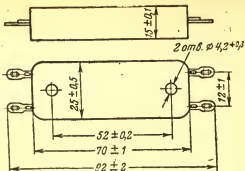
Габаритный чертеж столбов Д1009А, Д1011А.
